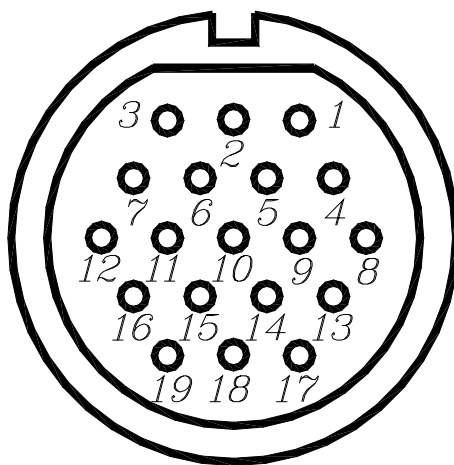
Нумерация контактов соединителя со стороны пайки
